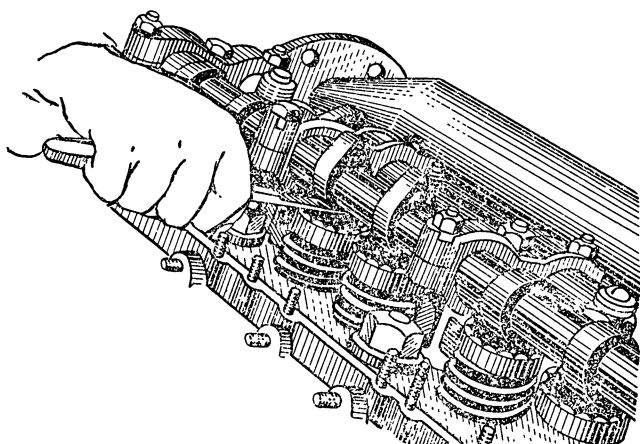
Проверка зазоров между затылками кулачков и тарелями клапанов
